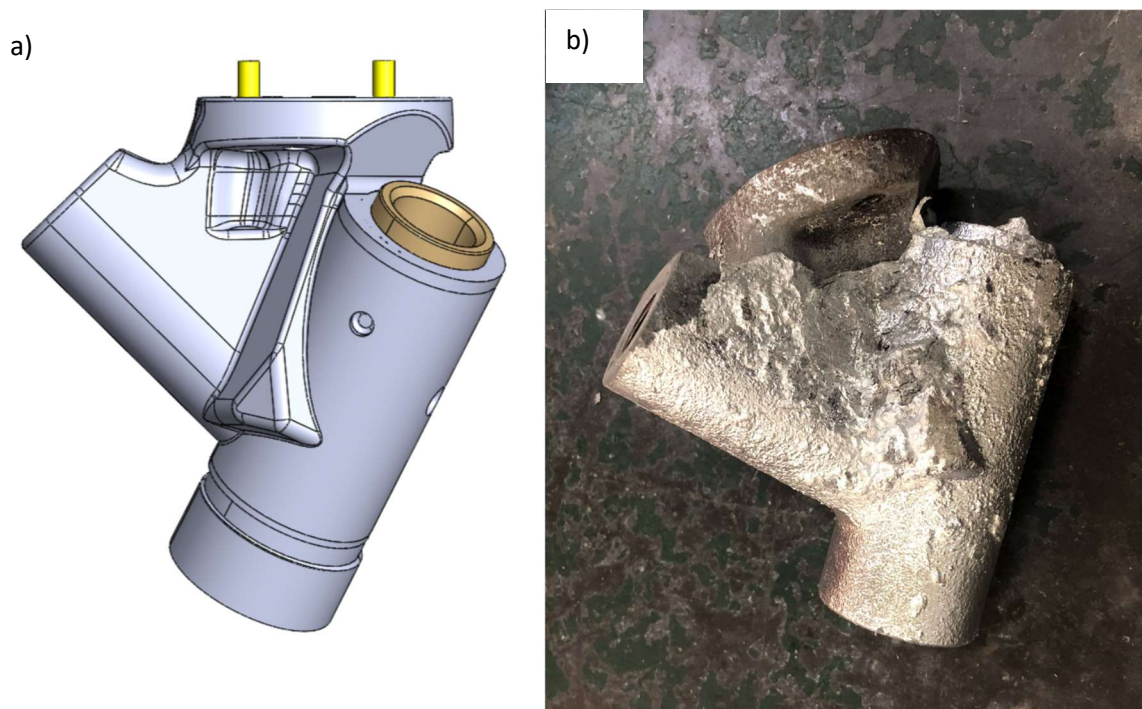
a) Bomba de injeção em CAD, b) bomba de injeção para recondicionar.
